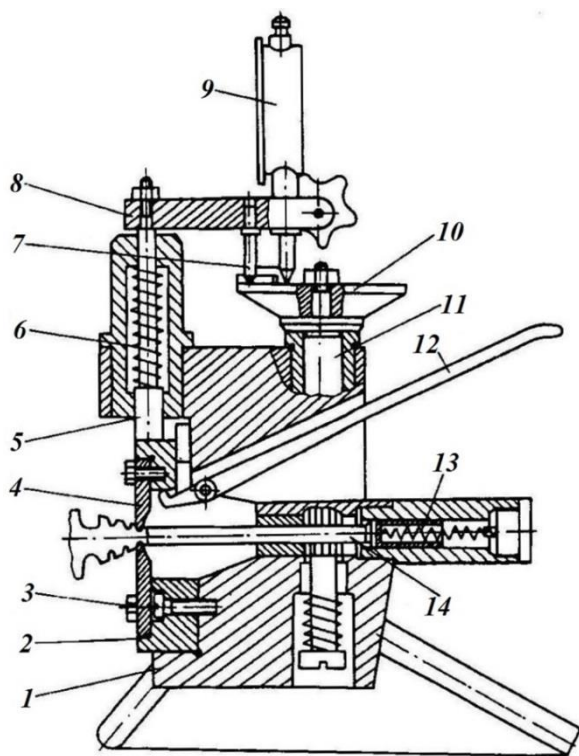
Индикаторный прибор для контроля размеров ёлочного замка
